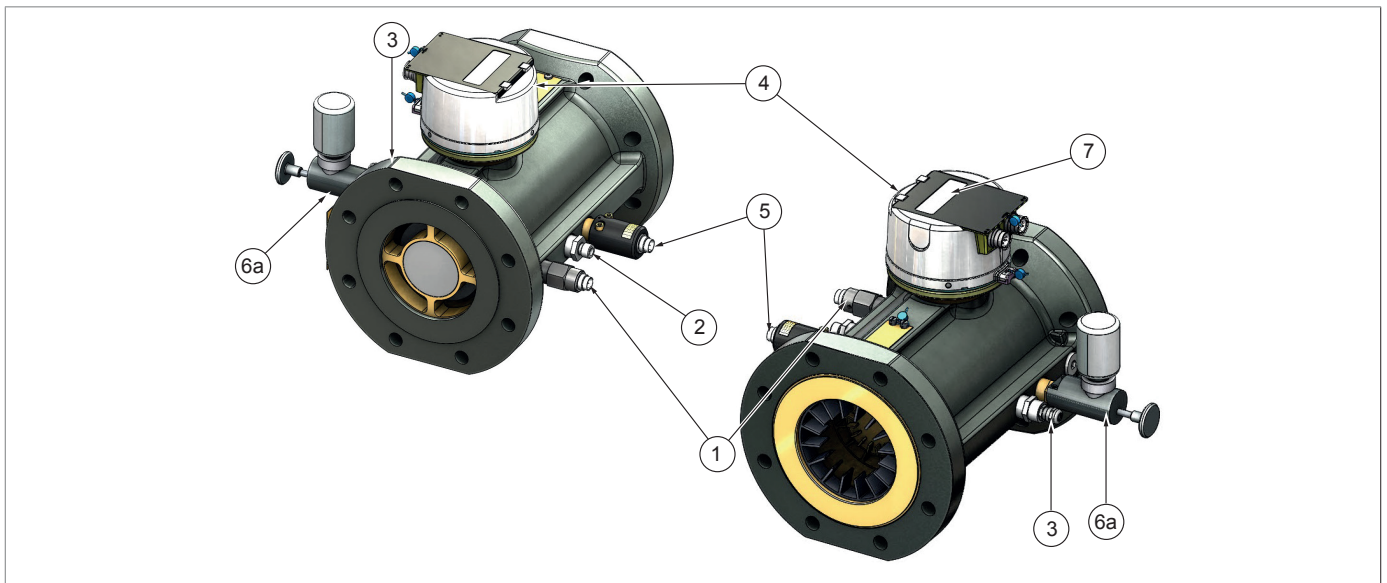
Posicionamiento de conexiones y accesorios del contador iM-TM cuerpo de aluminio
